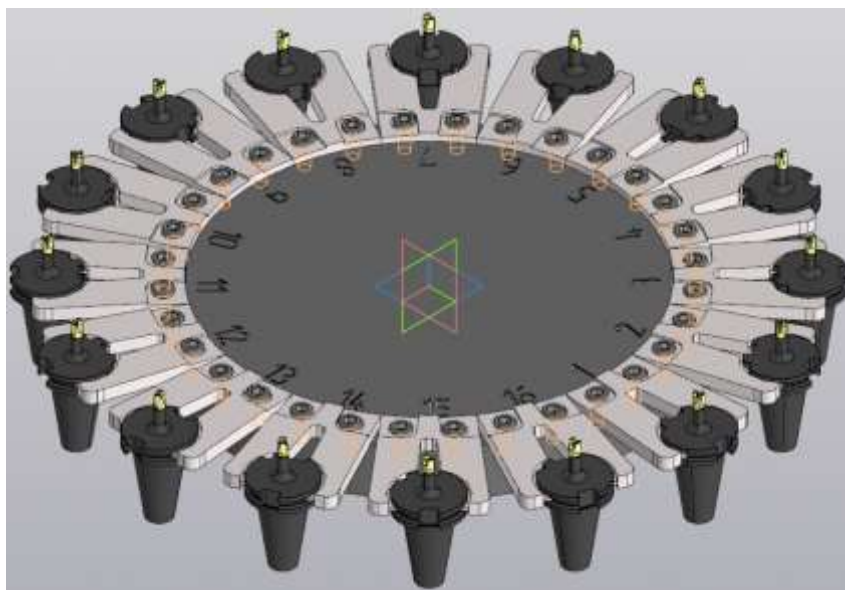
Предварительная твердотельная модель инструментального магазина малогабаритного фрезерного станка
